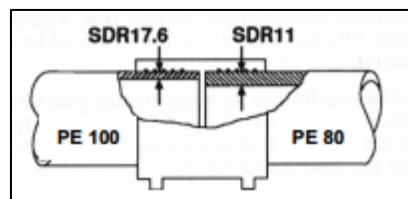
Soldadura amb tubs de diferent gruix.
